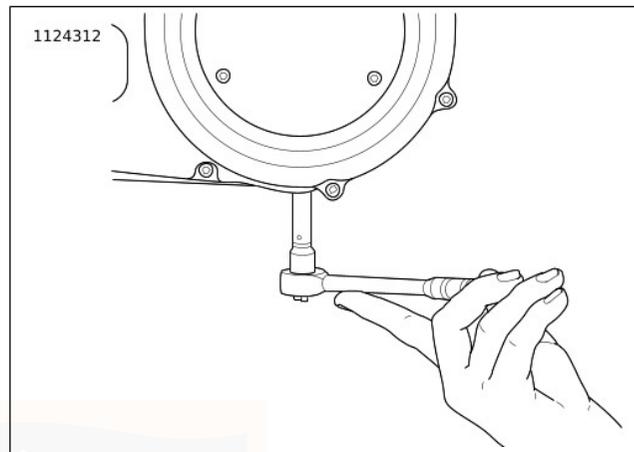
Ausbau/Einbau der Kettengehäuse-Ablassschraube
